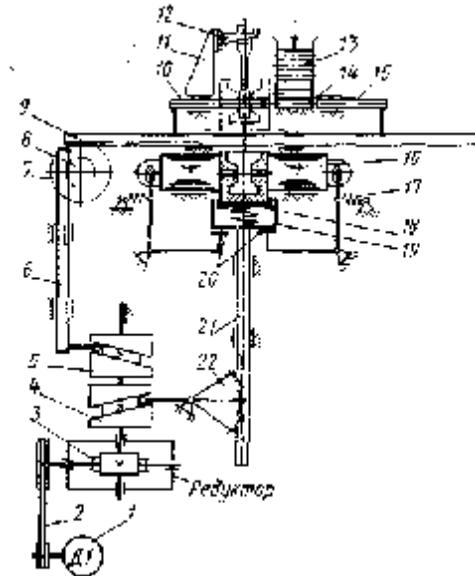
Кинематическая схема полуавтомата для сборки поршня с пальцем
